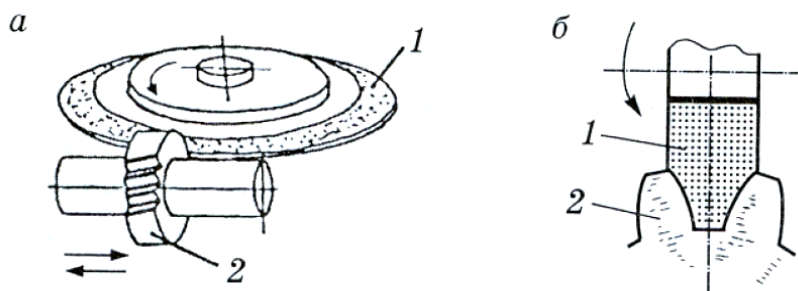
Шлифование зубьев методом копирования: а – схема шлифования фасонным кругом; б – профиль шлифовального круга; 1 – инструмент; 2 – обрабатываемое зубчатое колесо
